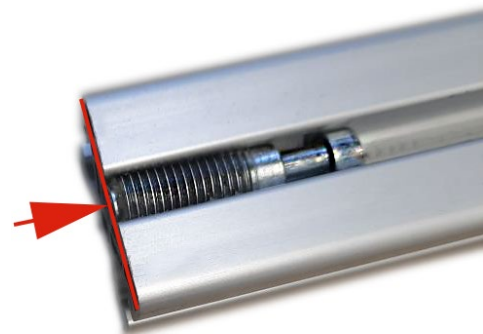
Gewindestück bündig zur Stirnfläche eindrehen
